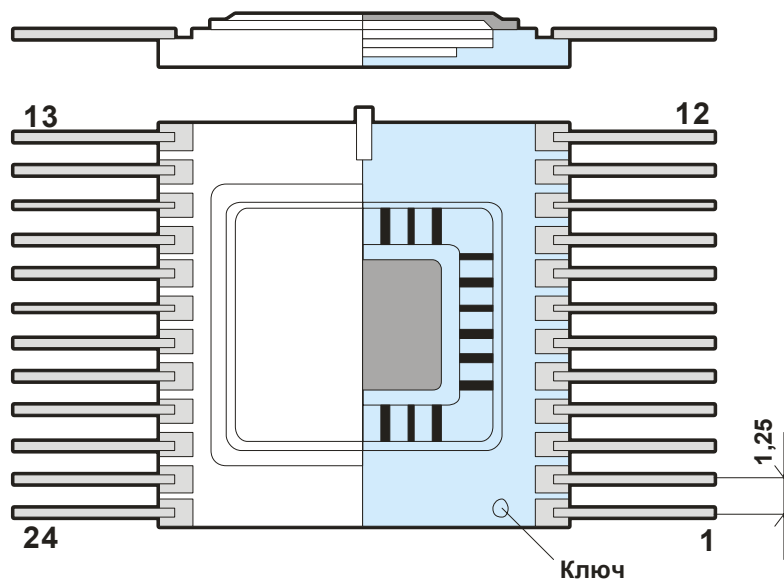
Конструкція металокерамічного корпусу 4118
